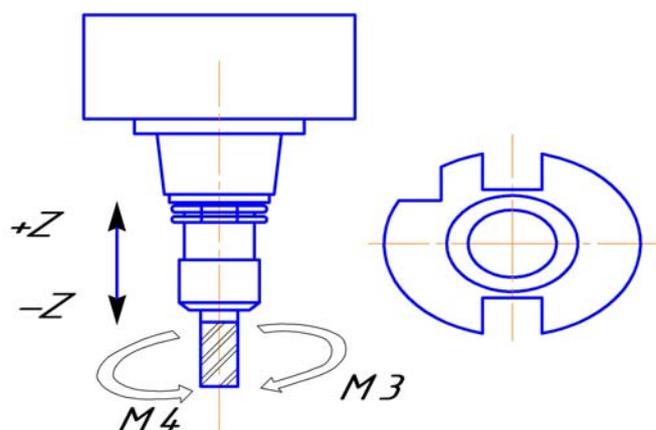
Направления вращения шпинделя фрезерного станка с ЧПУ
